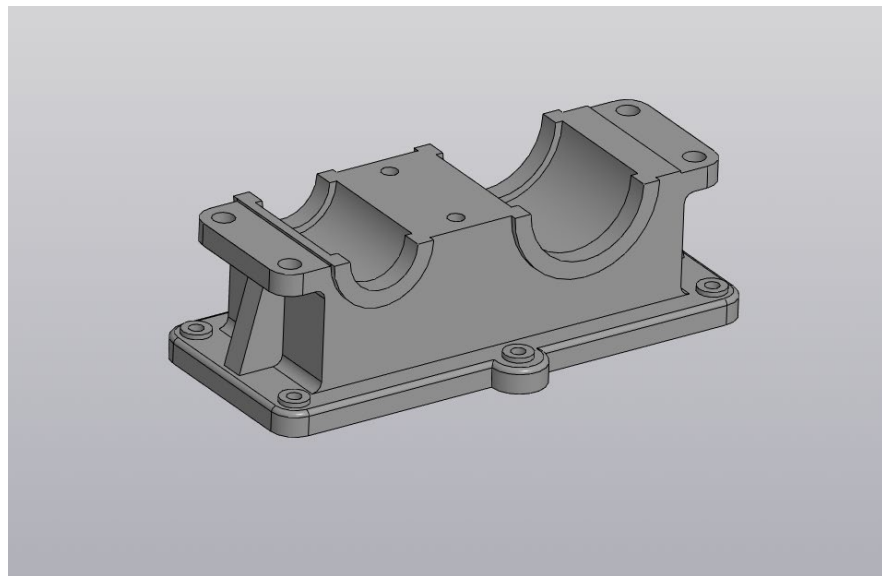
3D модель деталі «Корпус горизонтального редуктора»
